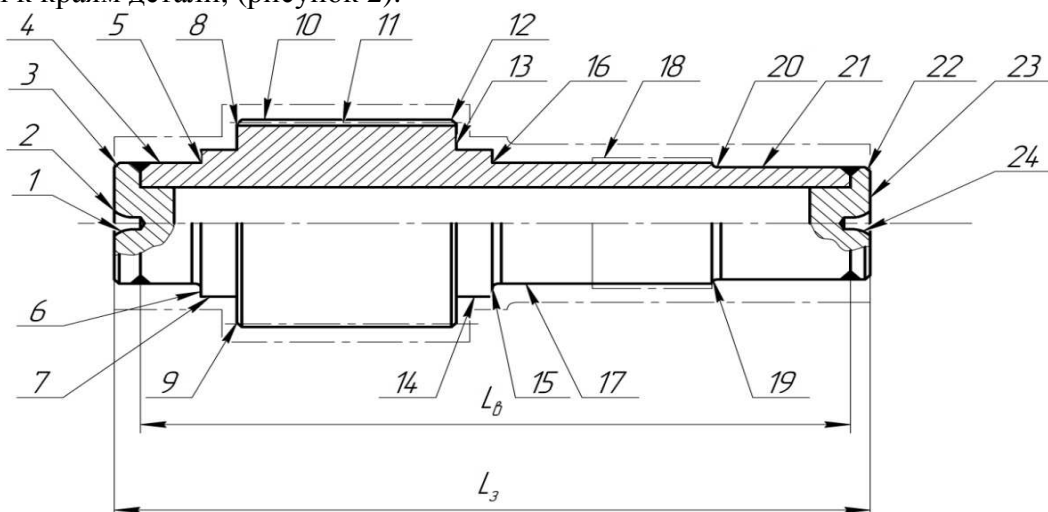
Эскиз сборно-сварной малоотходной пустотелой заготовки вала шлицевого
